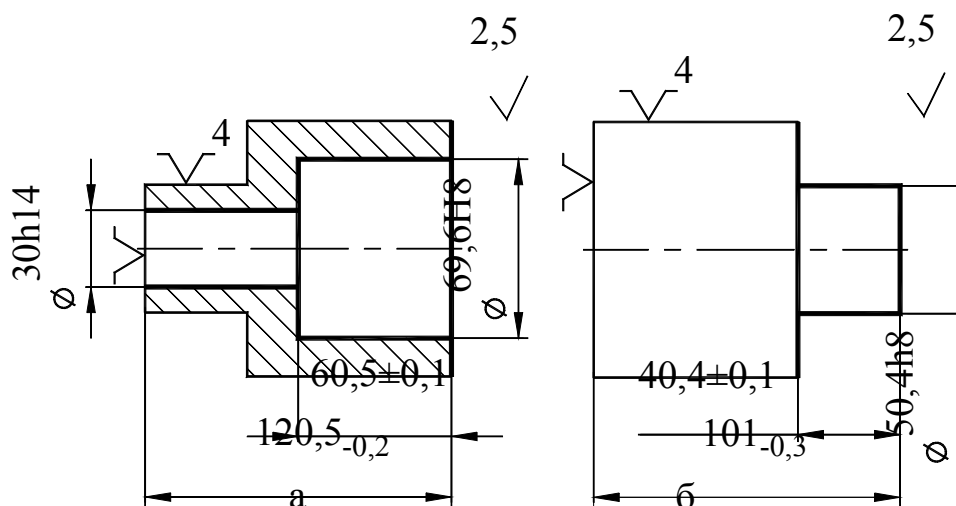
Обработка заготовки на станке с ЧПУ:
